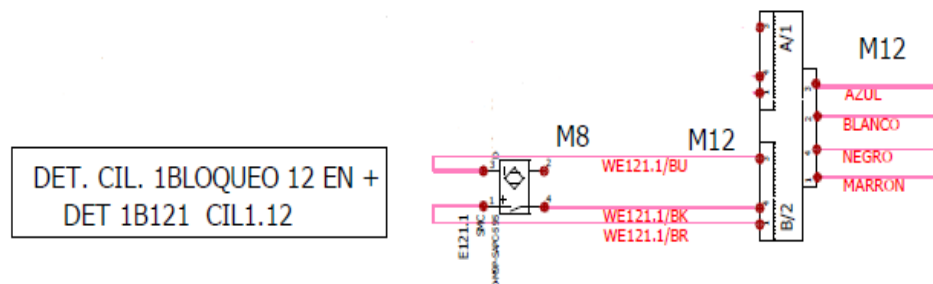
Conexiones Herramienta 12 EN + del Lado izquierdo.
